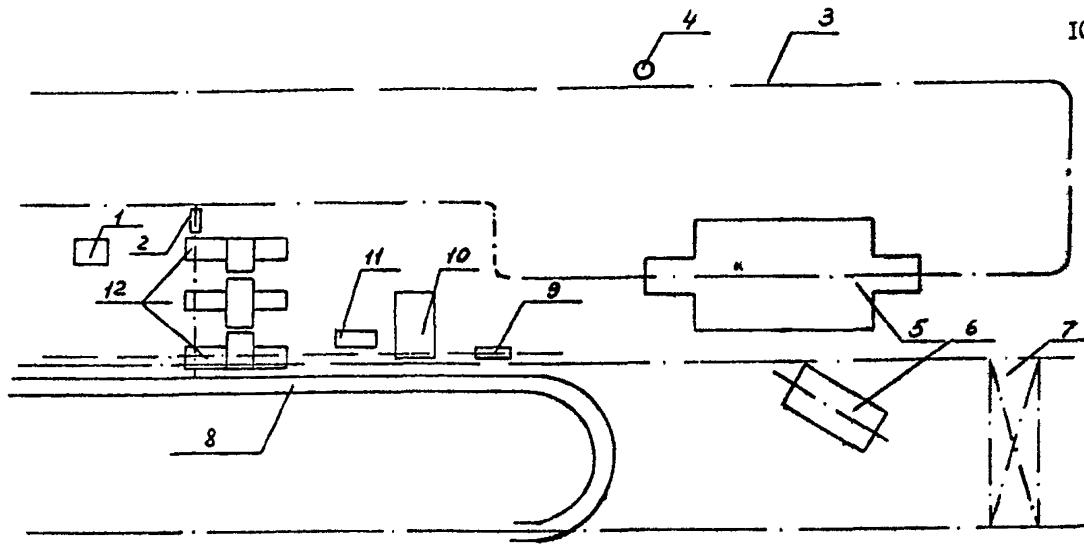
Типовая схема планировки рабочего места разборки двигателя
